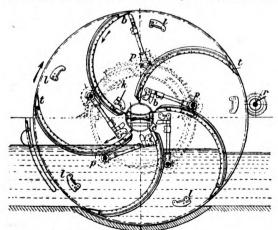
COUPE DU TAMBOUR ROTATIF A GRILLES, SYSTÈME GEIGER
